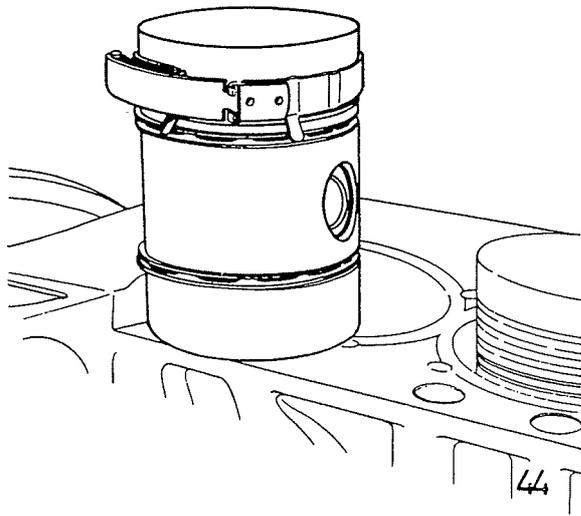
Eingebauter Kolben vor dem Aufsetzen des Zylinders
